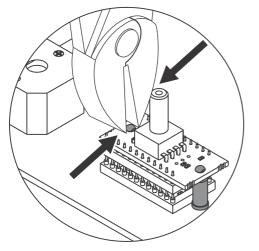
Демонтаж пьезоэлектрического датчика MSS PCB
